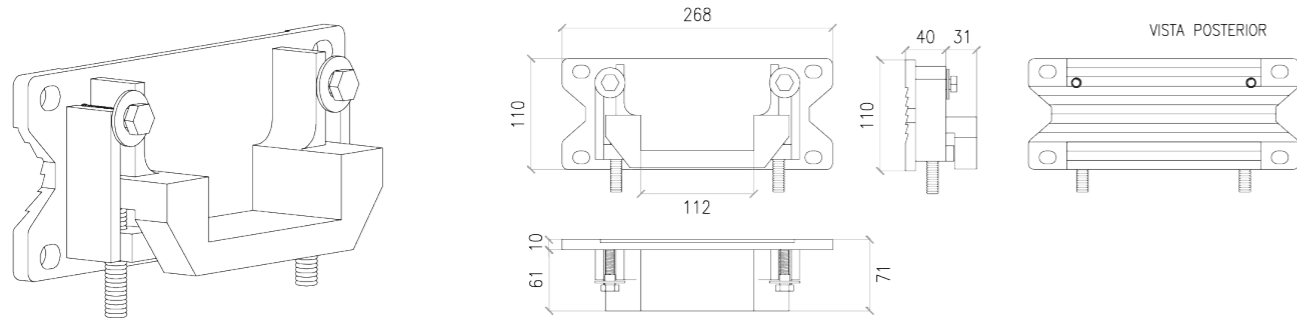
Detalle placa de anclaje universal tipo HERMS SP 3501.
